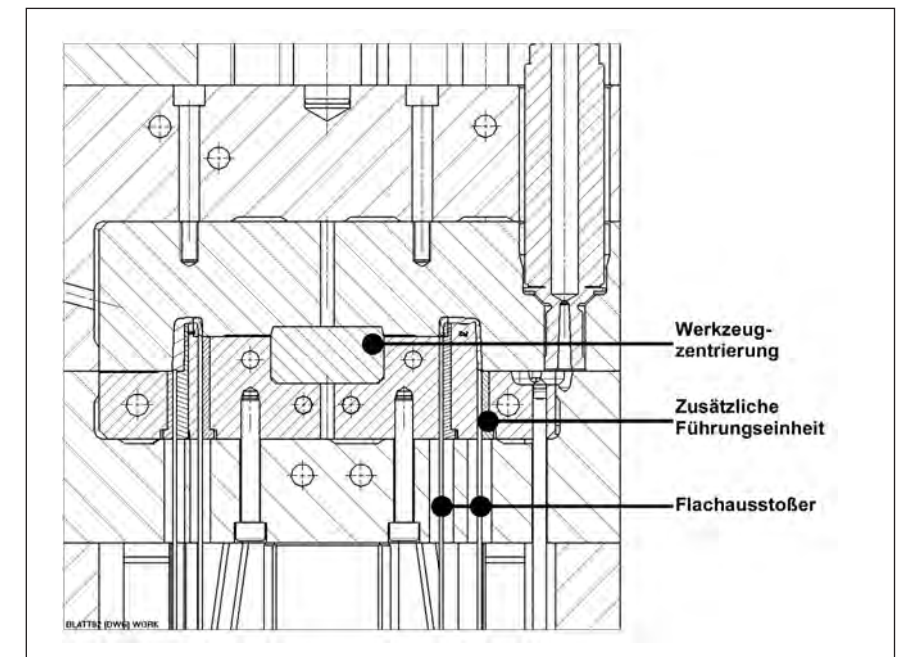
Schnittansicht durch das Werkzeug mit Flachauswerfer einschließlich der Zentrierung
